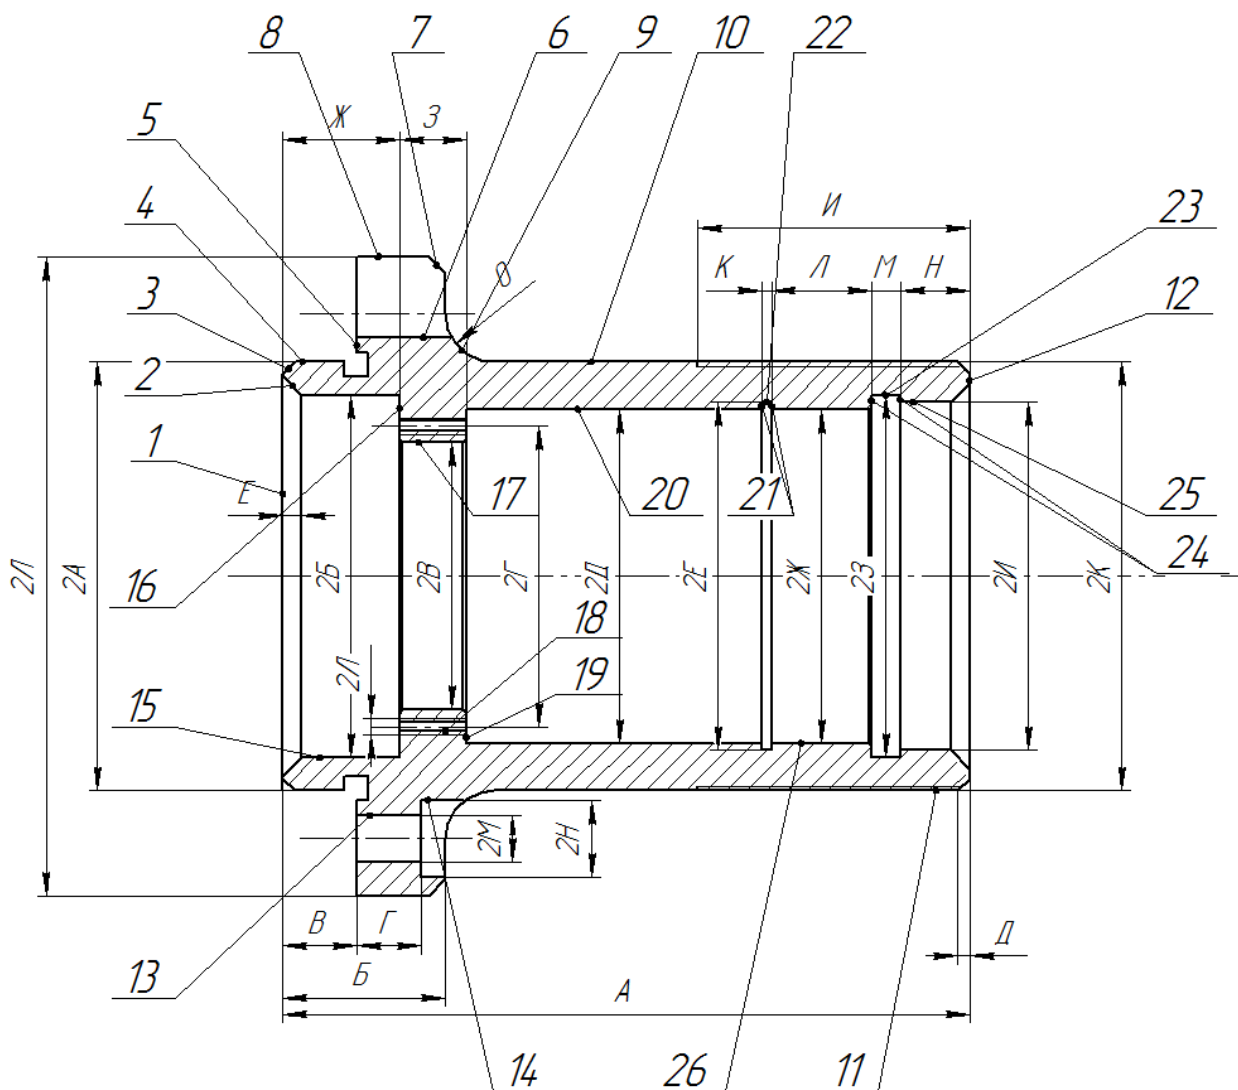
Эскиз корпуса с кодировкой размеров
